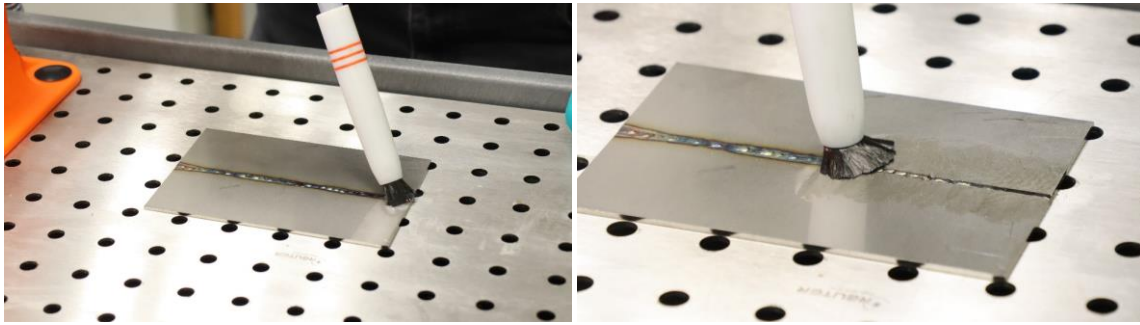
Durchführung der Schweißnahtreinigung an einem Blechcoupon 1.4404
